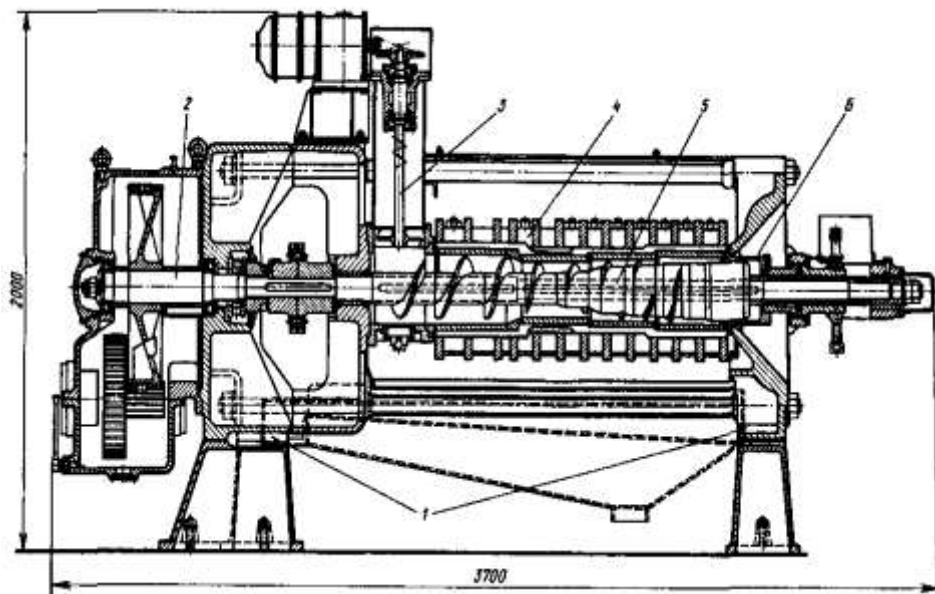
Конструктивна схема форпресу ФП [50]
